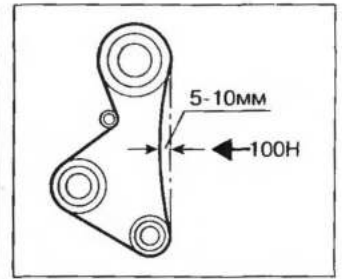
Схема проверки натяжения ремня механизма газораспределения
